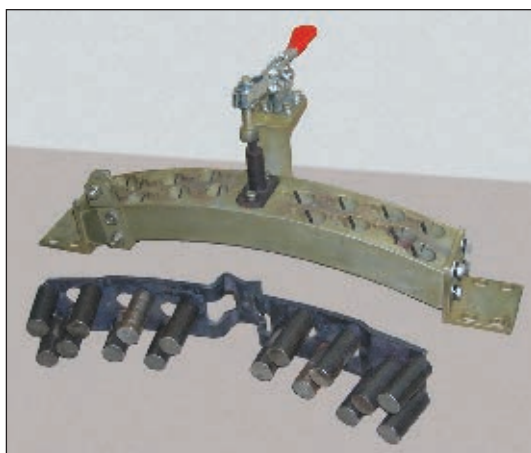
Каркас тормозной колодки и приспособление для сборки и сварки его деталей
